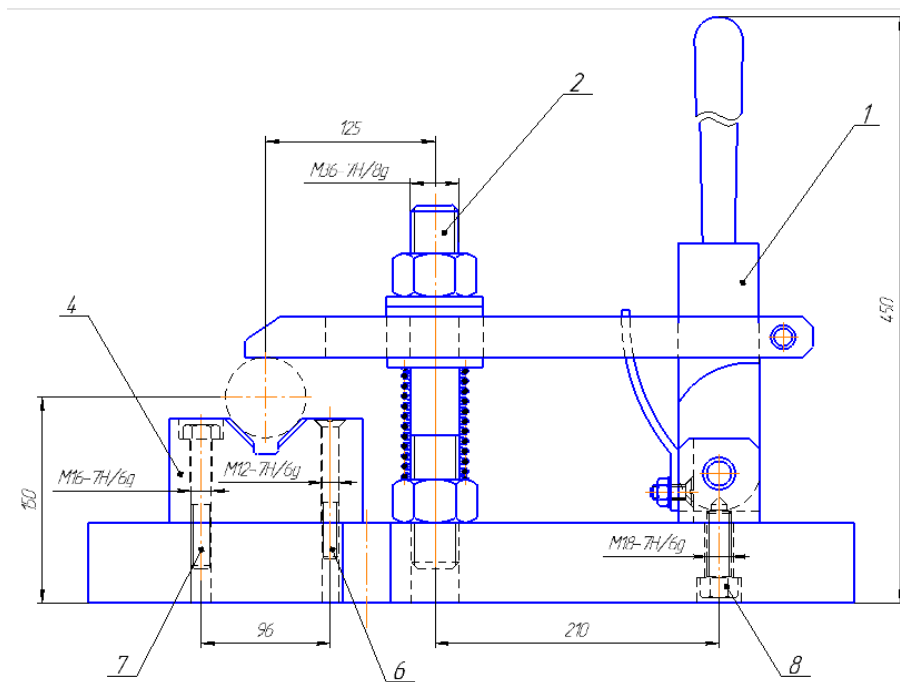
Схема станочного приспособления на отрезную операцию
